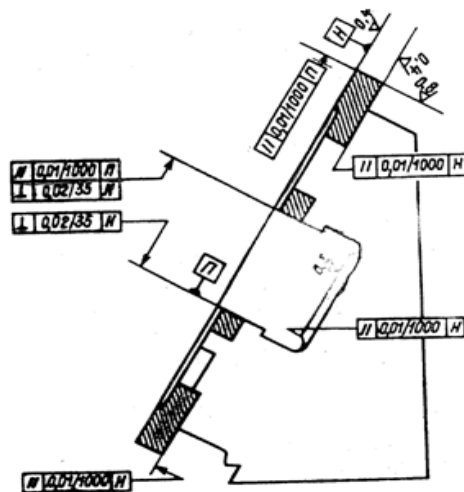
Технические требования к сборке накладных направляющих скольжения токарного станка класса П
